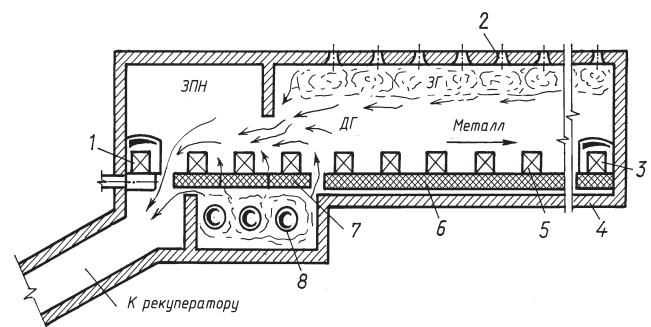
Схема нагревательной печи стана 320/150: 1 – боковой посад заготовок; 2 – сводовая плоскопламенная горелка; 3 – боковая выдача заготовок; 4 – обмуровка печи; 5 – нагреваемая заготовка; 6 – участок шагающего пода; 7 – шагающие балки; 8 – боковая длиннофакельная горелка; ЗПН – зона предварительного нагрева; ЗГ – зона горения; ДГ – дымовые газы
